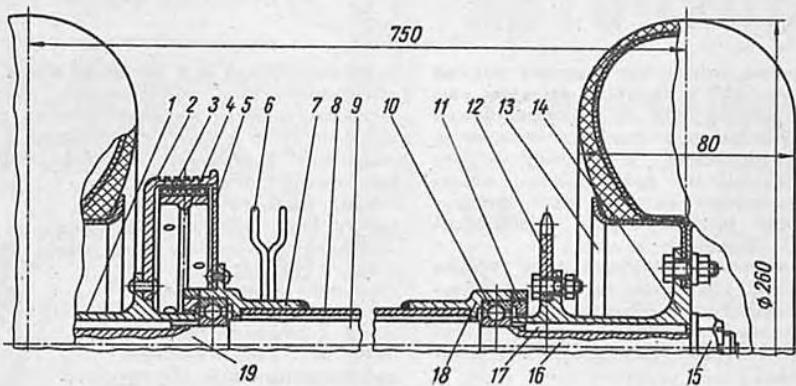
Задний мост: 1 — левая ступица (сталь 3 или сталь 45); 2 — тормозной барабан (К-125); 3 — тормозная накладка; 4 — тормозная колодка; 5 — опорный тормозной диск; 6 — рычажок тормозного кулака; 7 — левая подшипниковая опора; 8 — труба (элемент рамы); 9 — вал (сталь 18ХНВА); 10 — подшипник № 202; 11 — резьбовая шайба; 12 — цепная звездочка ($Z_2=24$); 13 — диск колеса; 14 — ступица; 15 — гайка 1М12; 16 — правый хвостовик вала; 17 — шпонка; 18 — подшипниковая опора; 19 — левый хвостовик вала.
